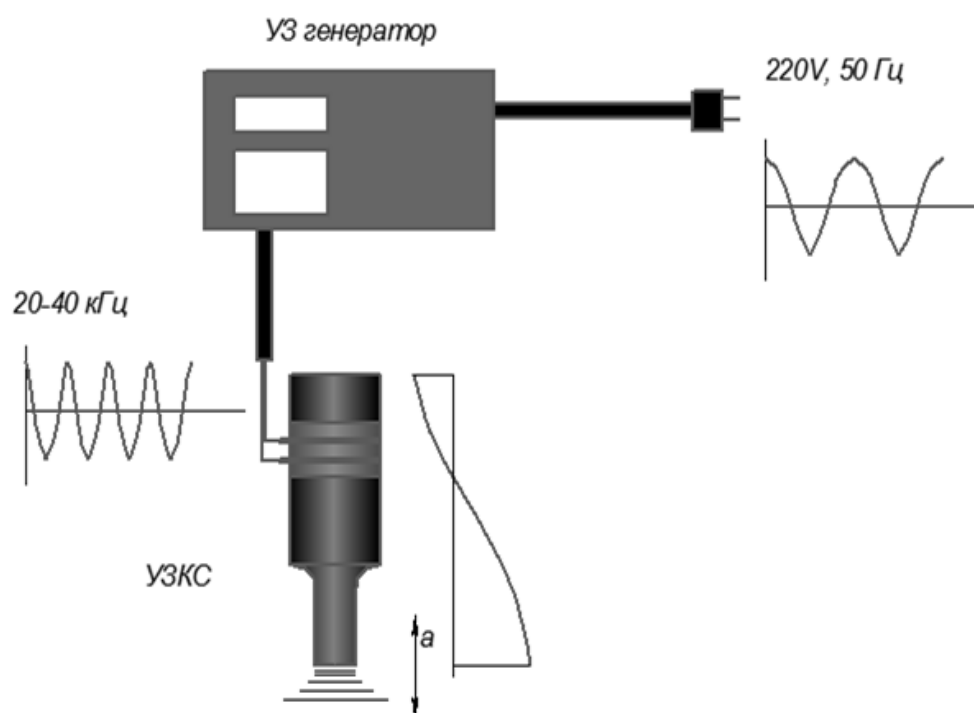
Структурная схема комплексов для ультразвуковой сварки
